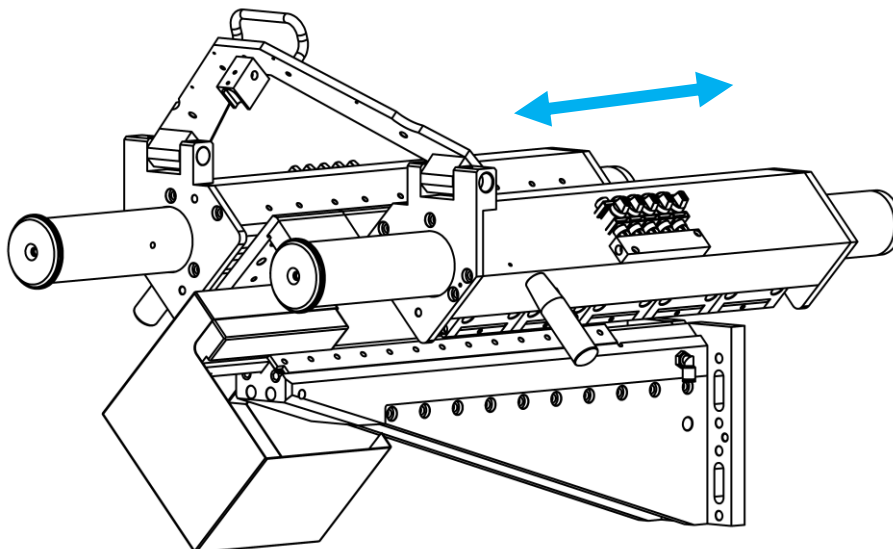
Verschiebbares Außenspannsystem mit Sonderinnenspannwerkzeug zum Einlegen abgekanteter Bauteile (max. 42 mm) bis 200 mm Schweißlänge, ohne Holmhub.
